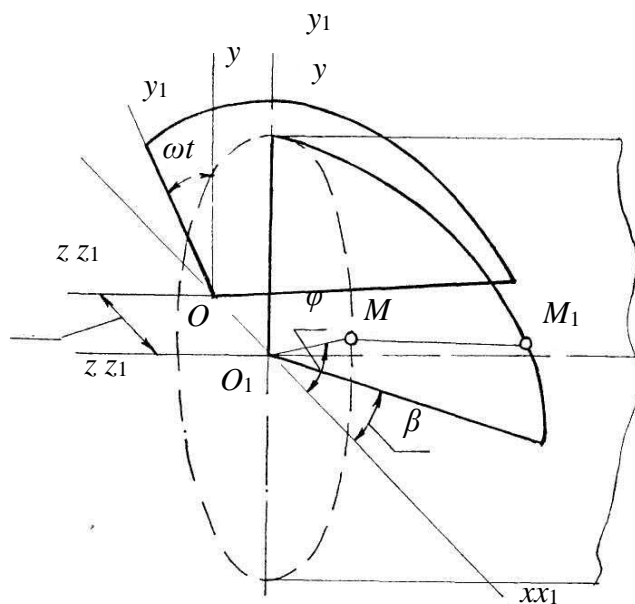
Схема движения точек фрезерных ножей зубцеобразной формы
